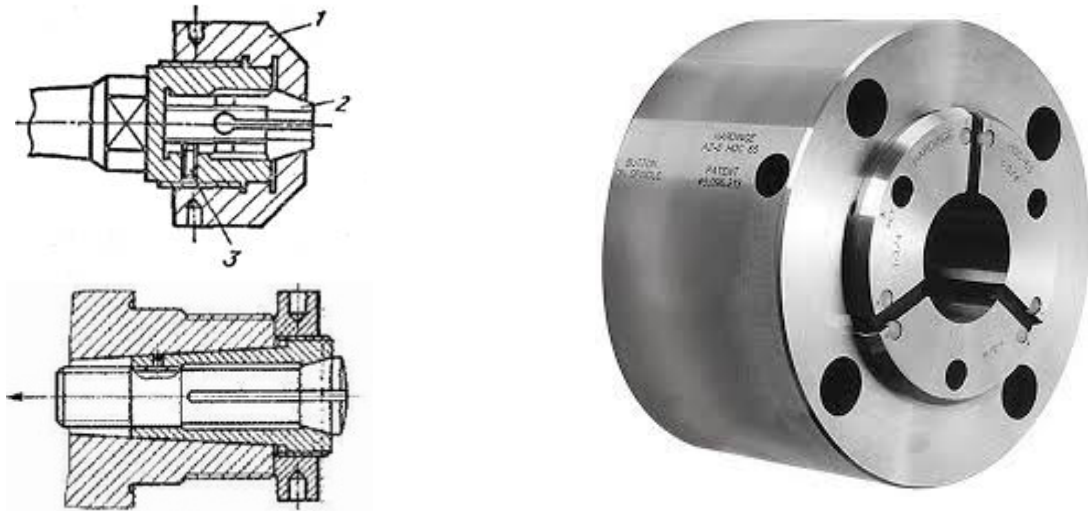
Цанговий патрон: 1 – затискна гайка, 2 – цанга, 3 – стопорний гвинт
